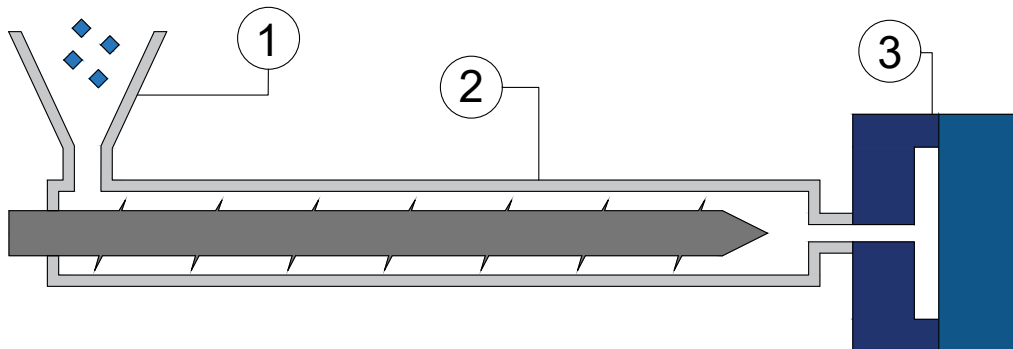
Croquis de una máquina de moldeo por inyección. Fuente propia.
